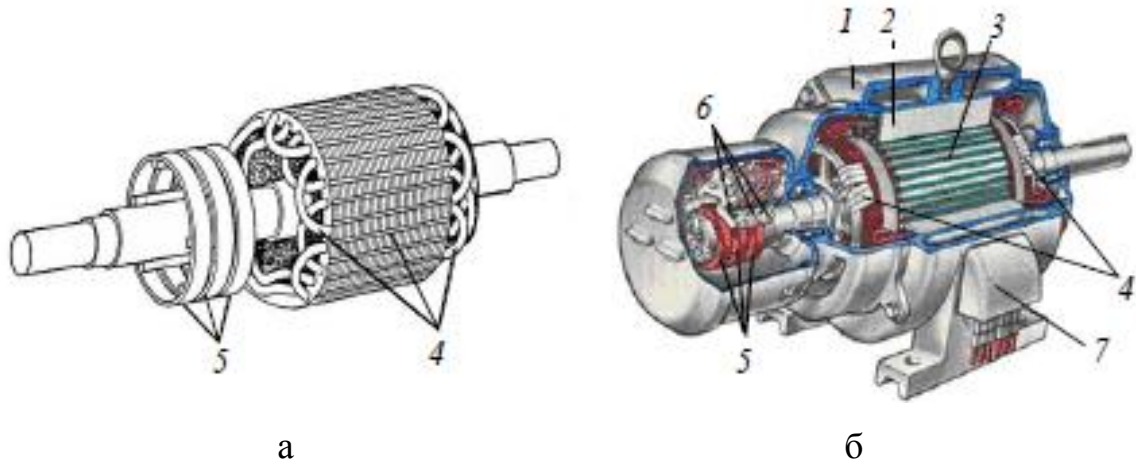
Общий вид фазного ротора (а) и асинхронной машины с фазным ротором в разрезе (б): 1 – станина; 2 – сердечник статора; 3 – сердечник ротора; 4 – обмотка ротора; 5 – контактные кольца; 6 – щетки; 7 – клеммная коробка.
